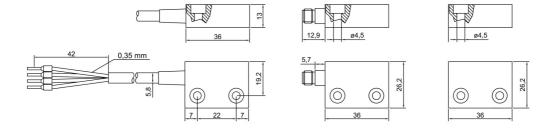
Dimensioni sensore ed attuatore MC336x
